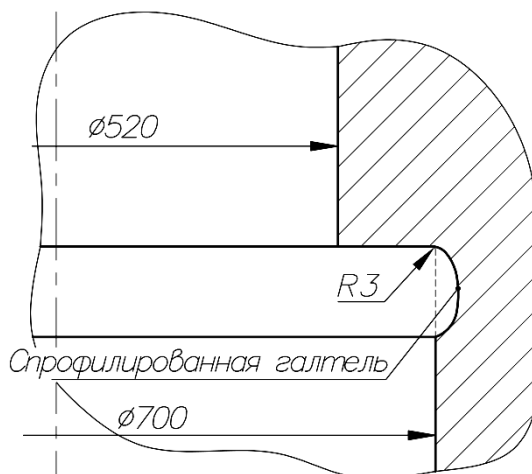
Конструкция галтельного перехода с заглублением в вертикальную стенку отверстия для установки гайки нажимного винта
